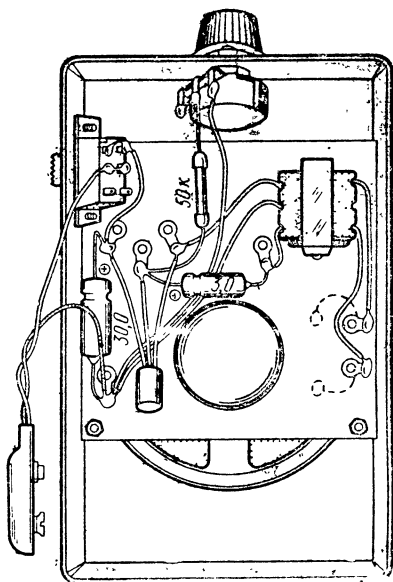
Размещение узлов и деталей схемы в корпусе метронома.
